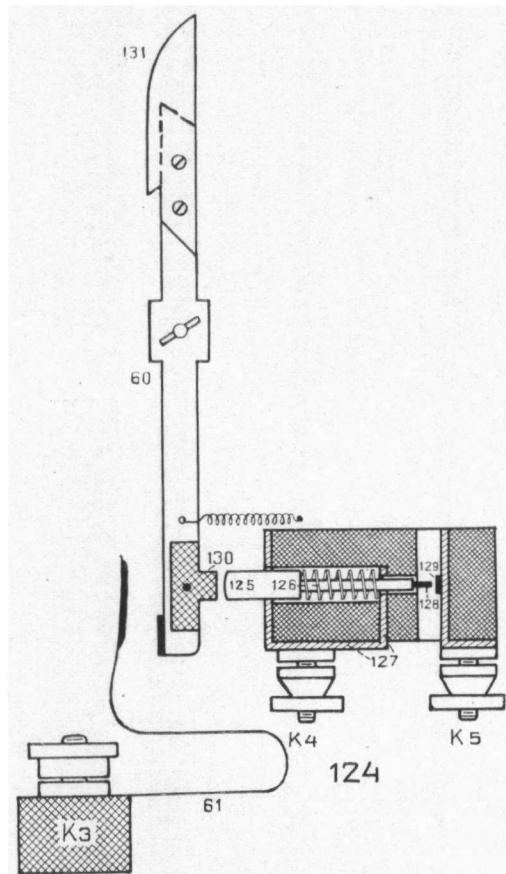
Hebel 60 mit Kontaktfeder 61 und horizontaler Durchschnitt durch den Druckschalter 124 hinterm Hebel.
